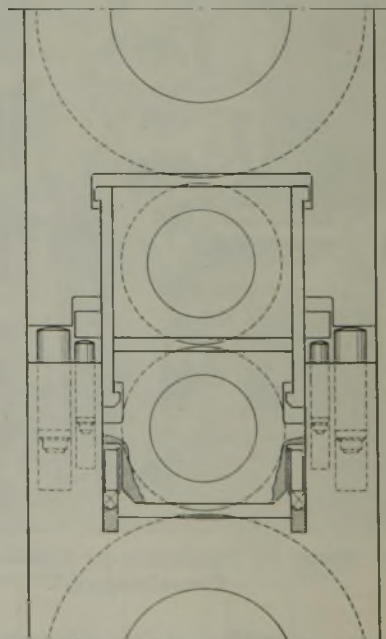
Gewichtsausgleich der Walzen eines Vierwälzengerüstes.
